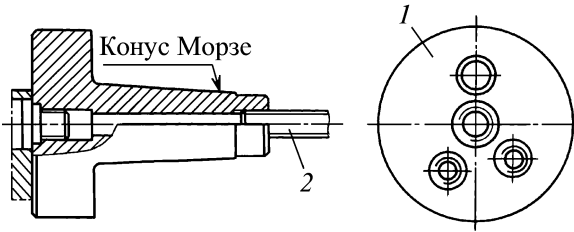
Планшайба для обработки корпусов и рычагов:
